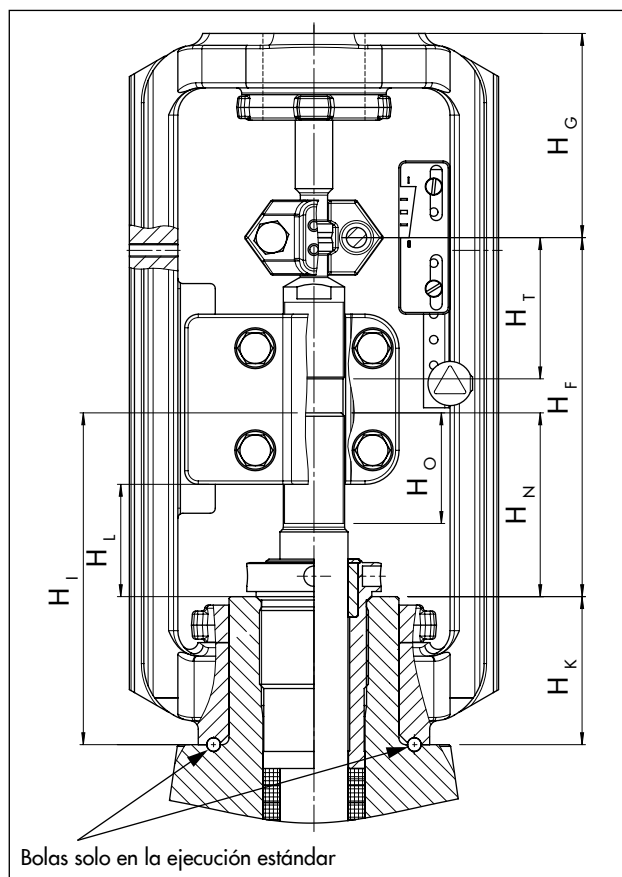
Dibujo dimensional con dimensiones de montaje de los accionamientos neumáticos Tipo 3271 y Tipo 3277
